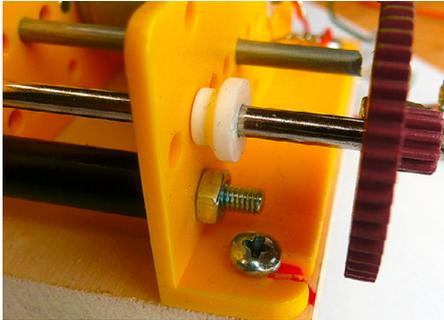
| Montageschraube klemmt das Zahnrad ein.
